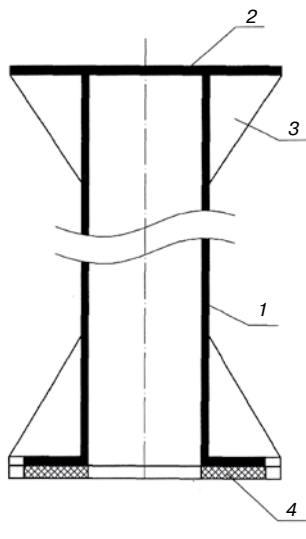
Погружающее приспособление: 1 – металлическая труба; 2 – верхний фланец; 3 – усиливающие ребра; 4 – нижний фланец с амортизирующей прокладкой
